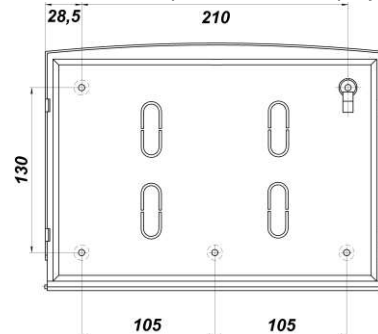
Розмітка отворів для кріплення корпусу ПКІ
